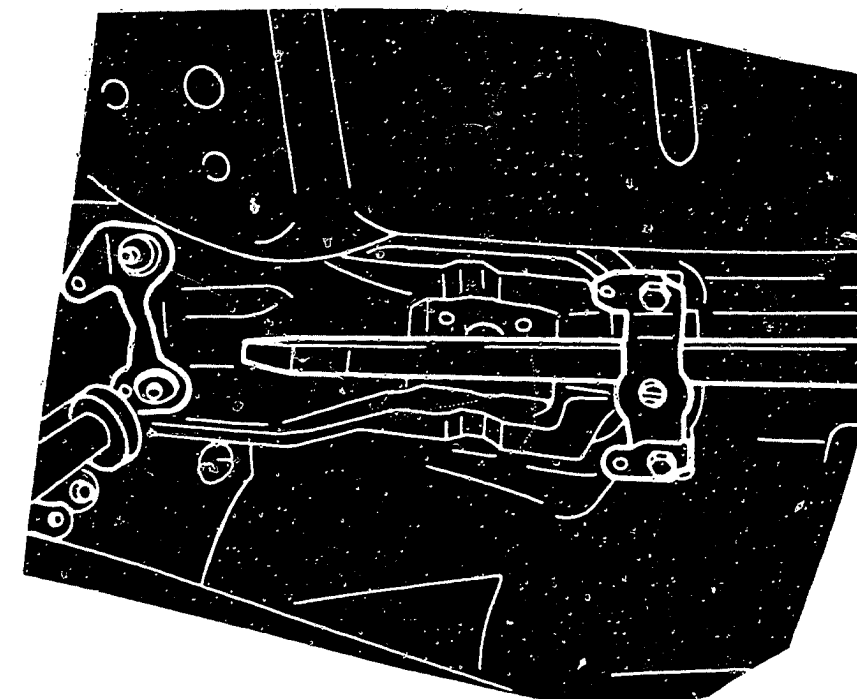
Unterstützen des Getriebegehäuseauslegers anlässlich der Getriebemontage.
